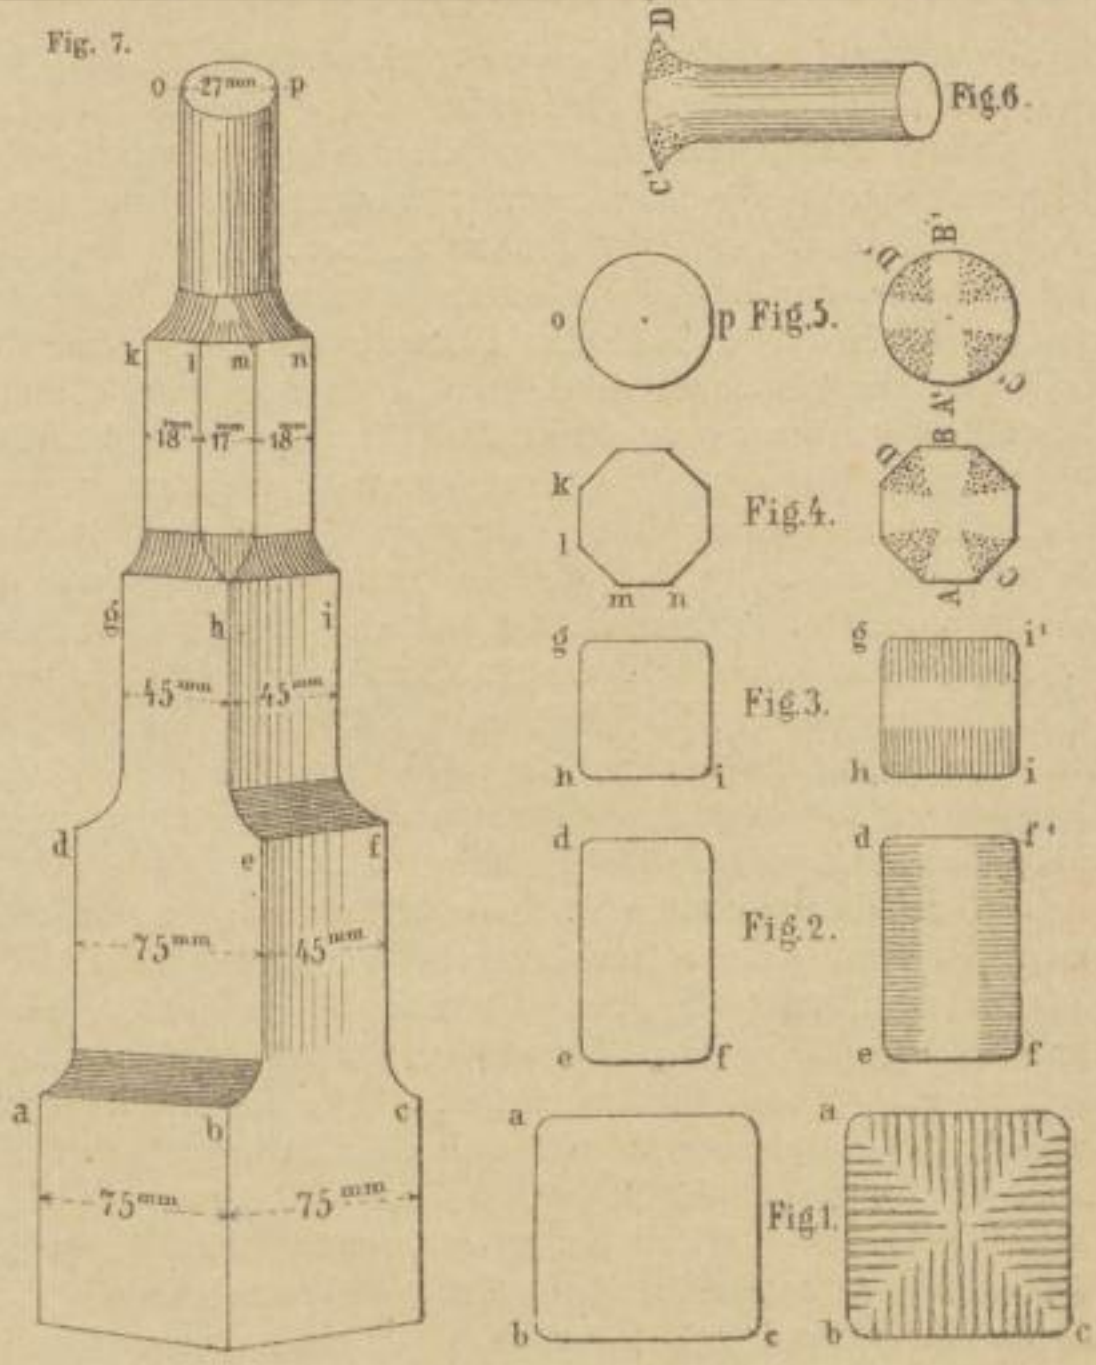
Zeichnung eines Rundmeißels, dessen Schneide nach der Richtung C' D' in der Fig. 5 gelegt ist. Waren die Ecken von richtiger Härte, so ging die Mitte der Schneide um. War die Mitte der Schneide richtig hart, so brachen die Ecken, weil zu hart, beim Härten oder beim Gebrauch eines solchen Bohrmeißels aus.
